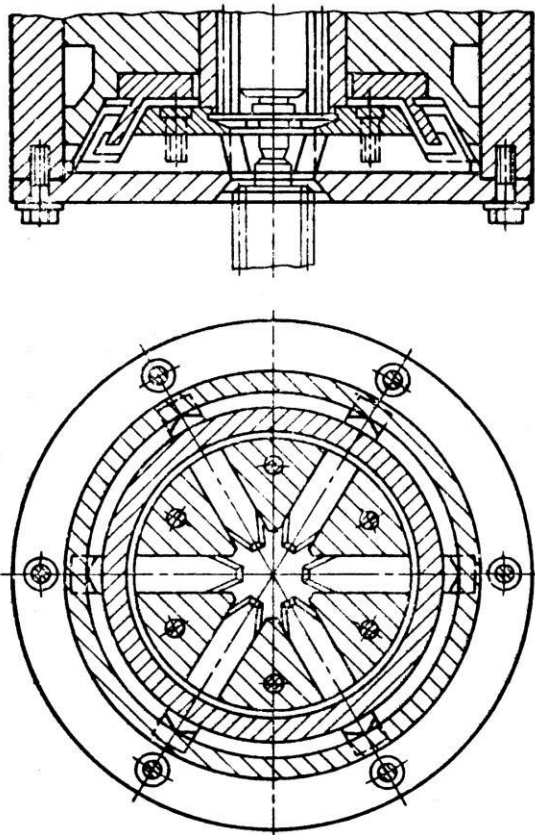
Різцева головка шліцьостругального верстата
